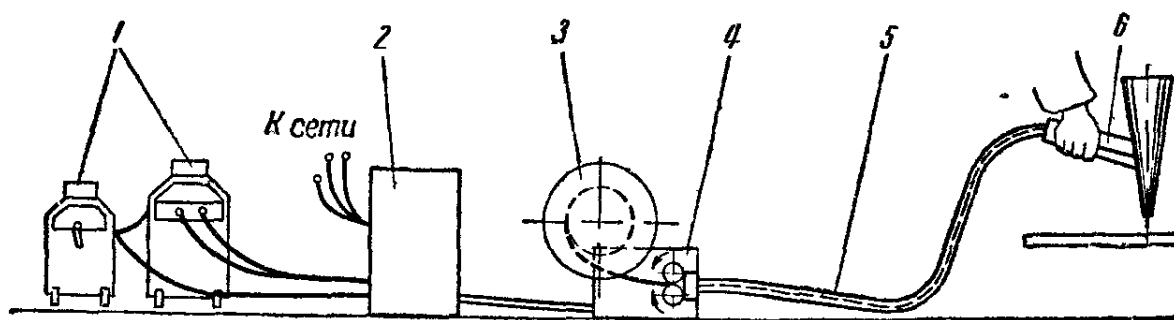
Схема полуавтоматической сварки под флюсом
